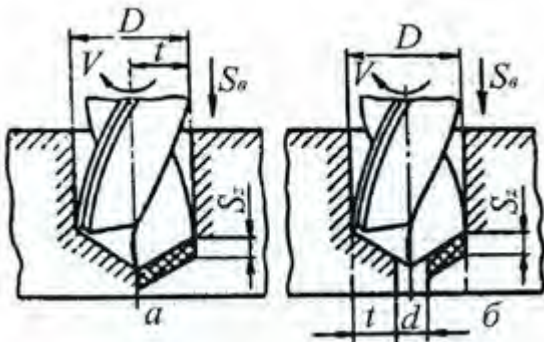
Схеми свердління (а) і розсвердлювання (б)
